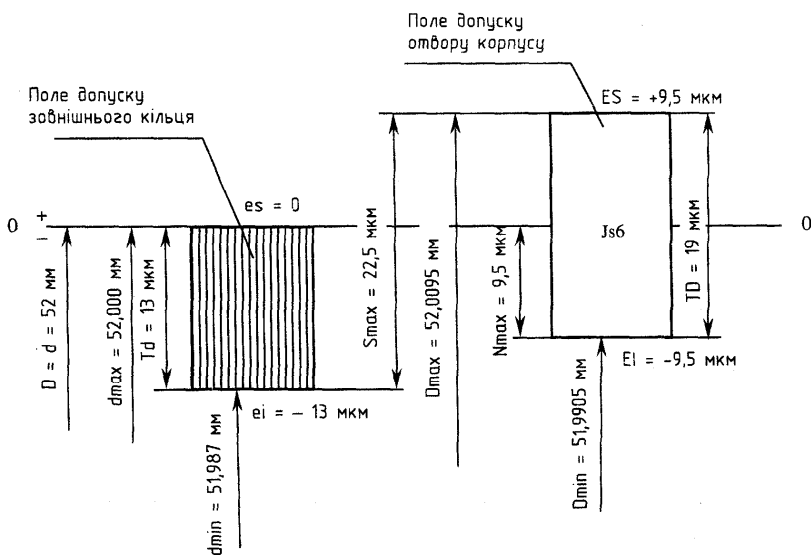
Схема розташування полів допусків у спряженні зовнішнього кільця підшипника з отвором корпусу
